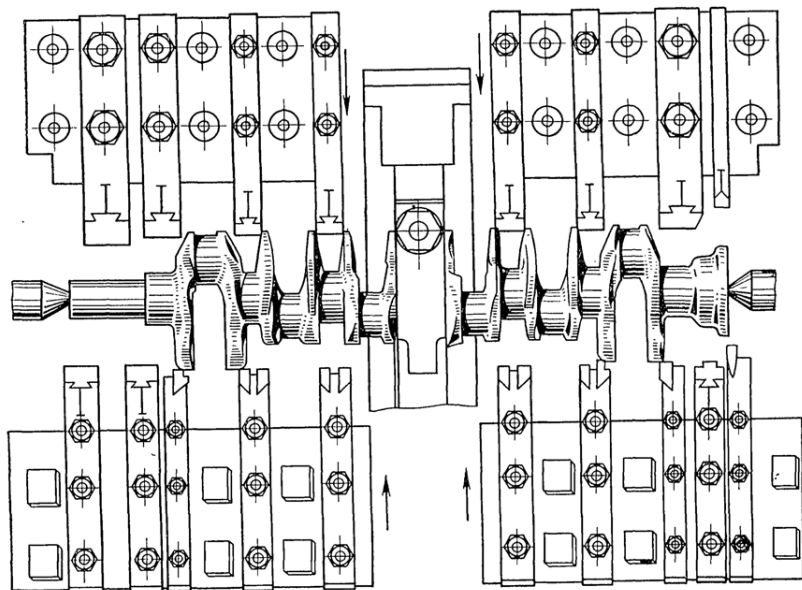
Эскиз наладки токарного многорезцового станка для обтачивания коренных шеек (кроме средней), ступенчатого конца, фланца и подрезания торцов и галтелей
